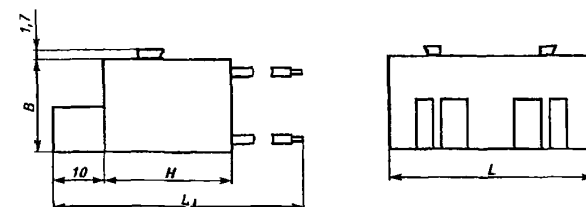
Габаритные и установочные размеры ограничителей перенапряжений типа ОПН 1
